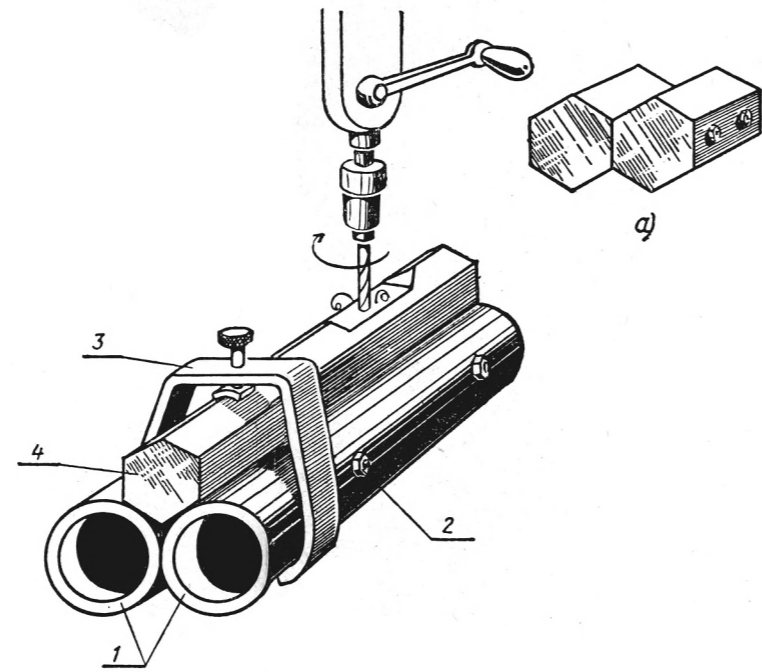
Призма из труб: 1 — трубы; 2 — болты; 3 — скоба; 4 — изделие
